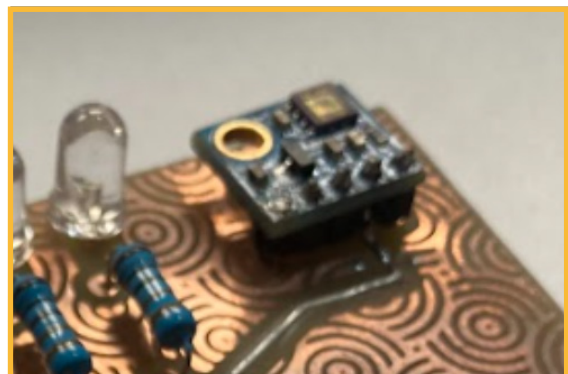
Sensor UV soldado. Elaboración propia.
